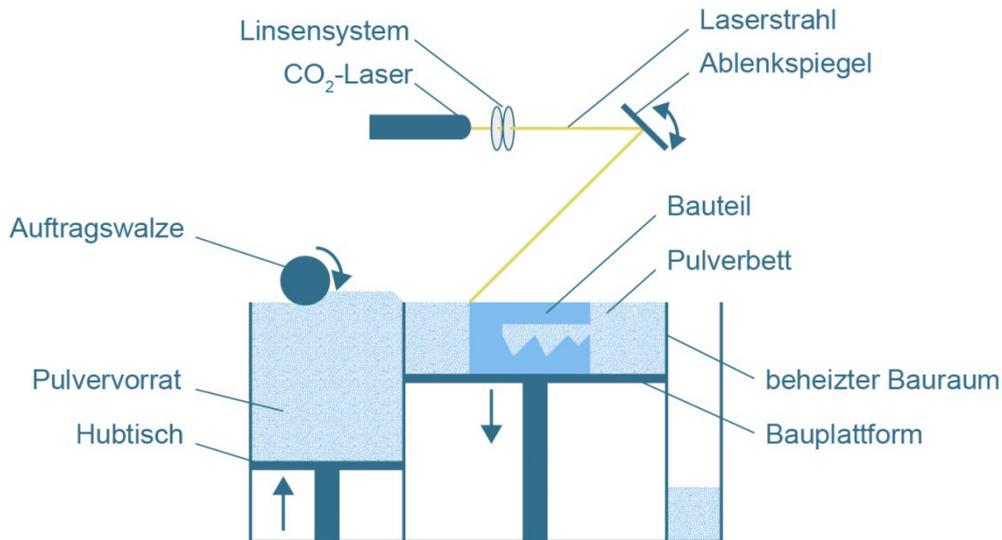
Aufbau und Elemente einer Laser-Sinter-Anlage
